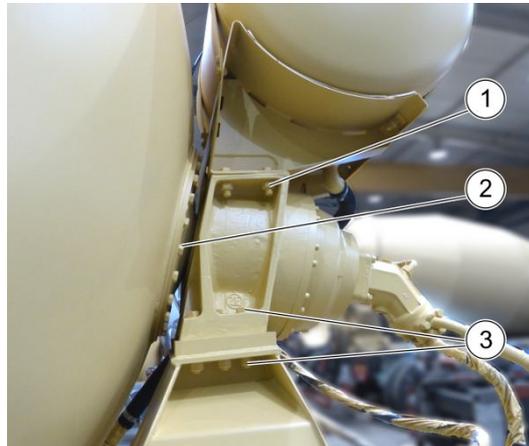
Schraubverbindungen am Getriebestützbock und am Getriebeflansch
